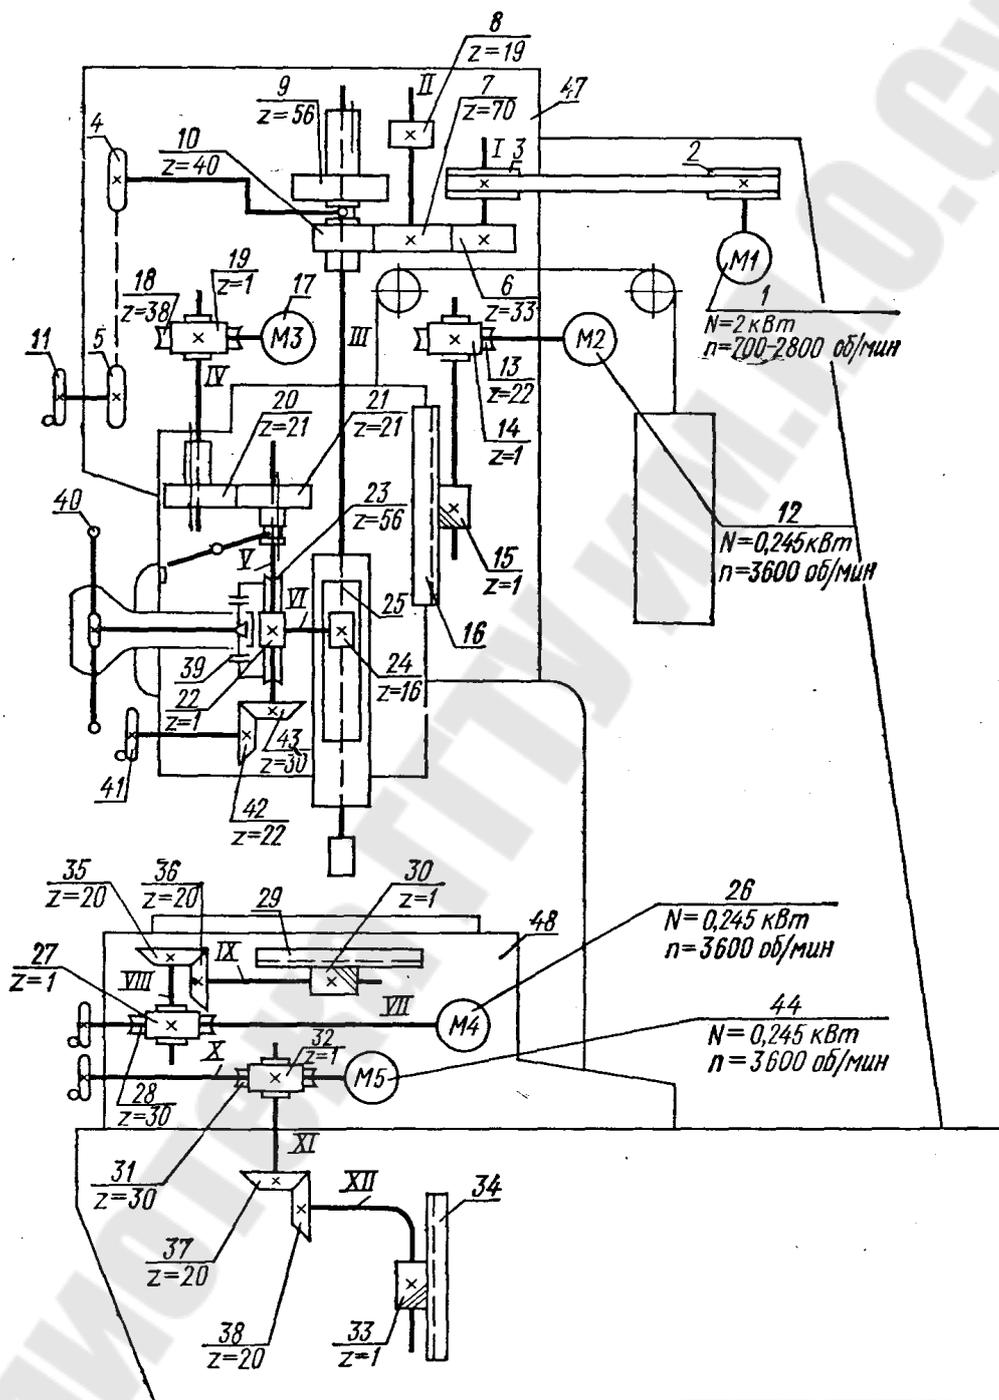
Кинематическая схема координатно-расточного станка
